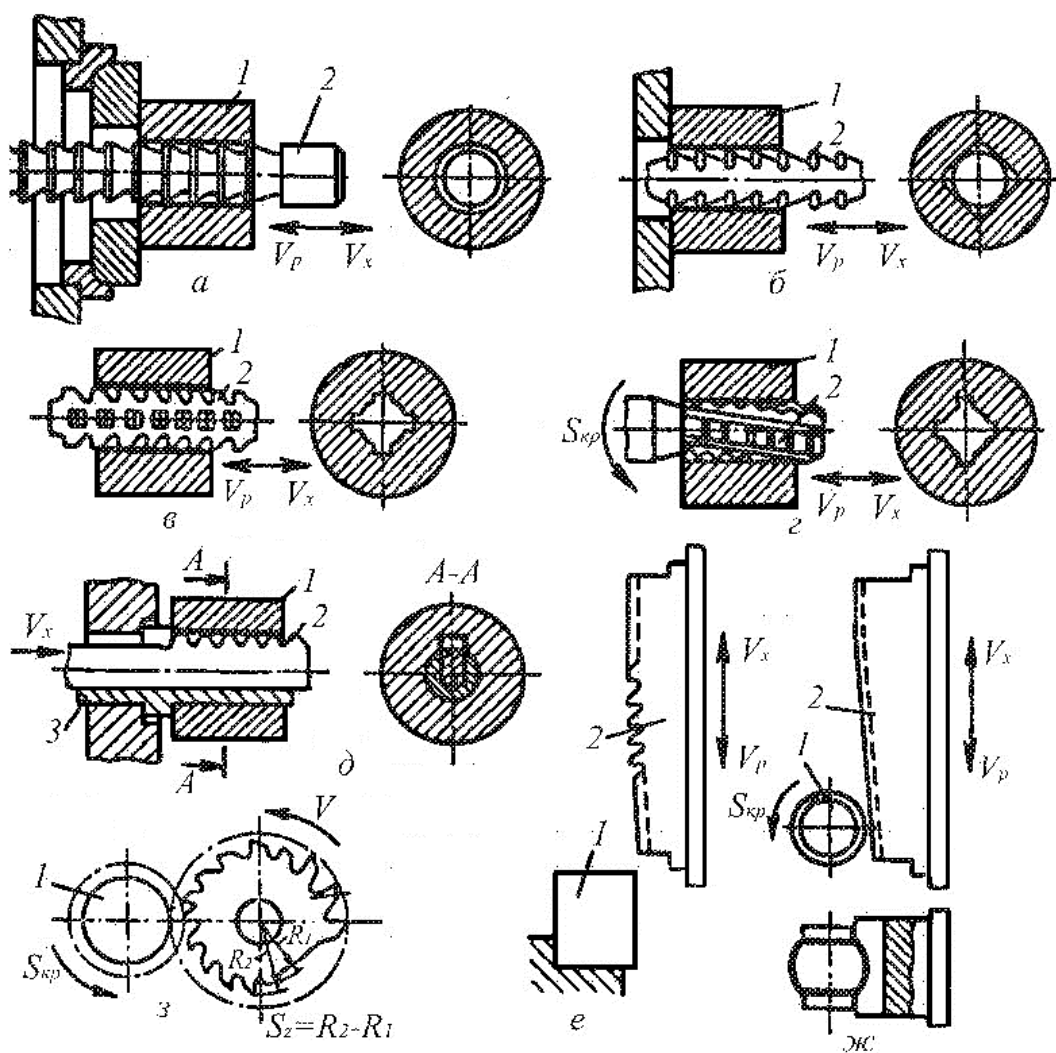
Схеми обробки поверхонь заготовок на протяжних верстатах
